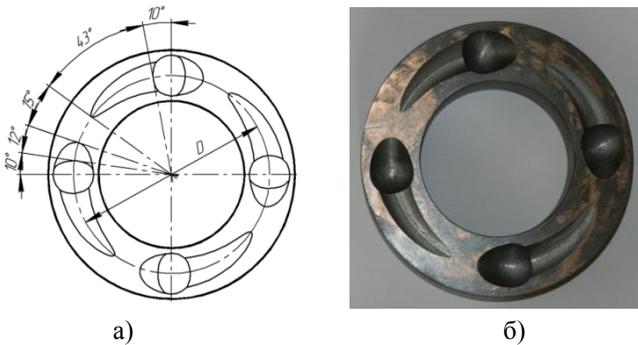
Конструктивна схема (а) та загальний вигляд (б) робочої поверхні ведучої півмуфти запобіжної муфти
